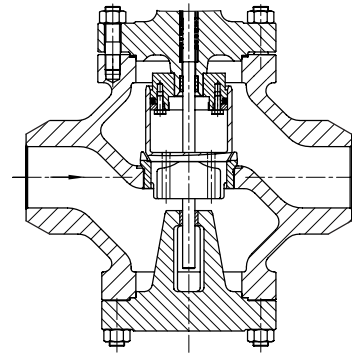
· Valvola Tipo 3254 con attacchi a saldare ed otturatore bilanciato
